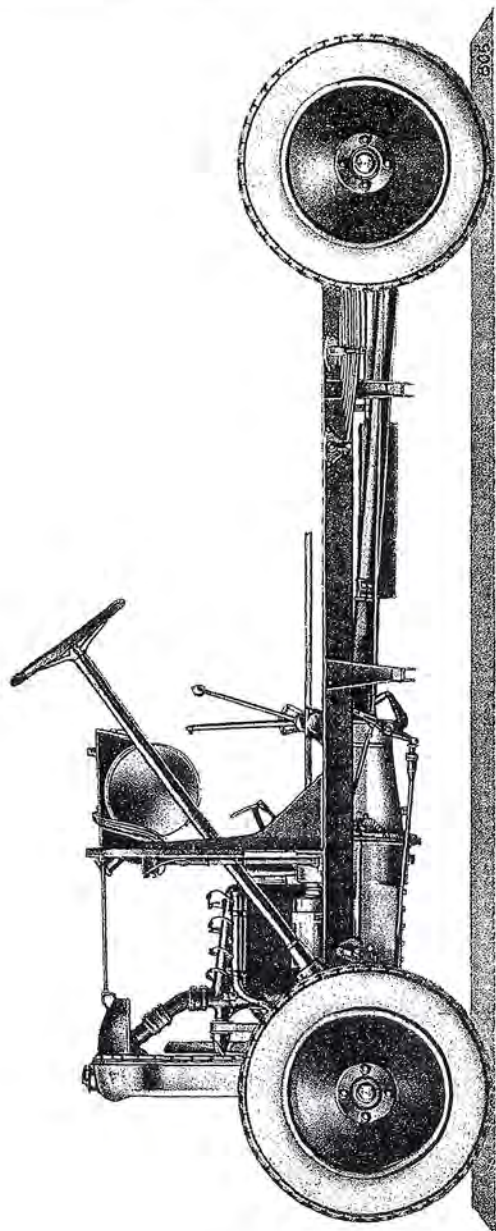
VUE EN ÉLEVATION DU CHASSIS 9 CH.
